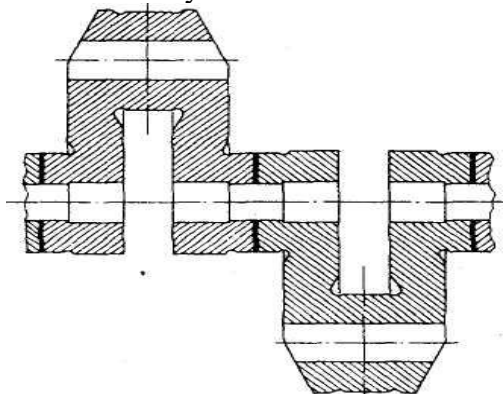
Сварной коленчатый вал дизелей МС/МСЕ
